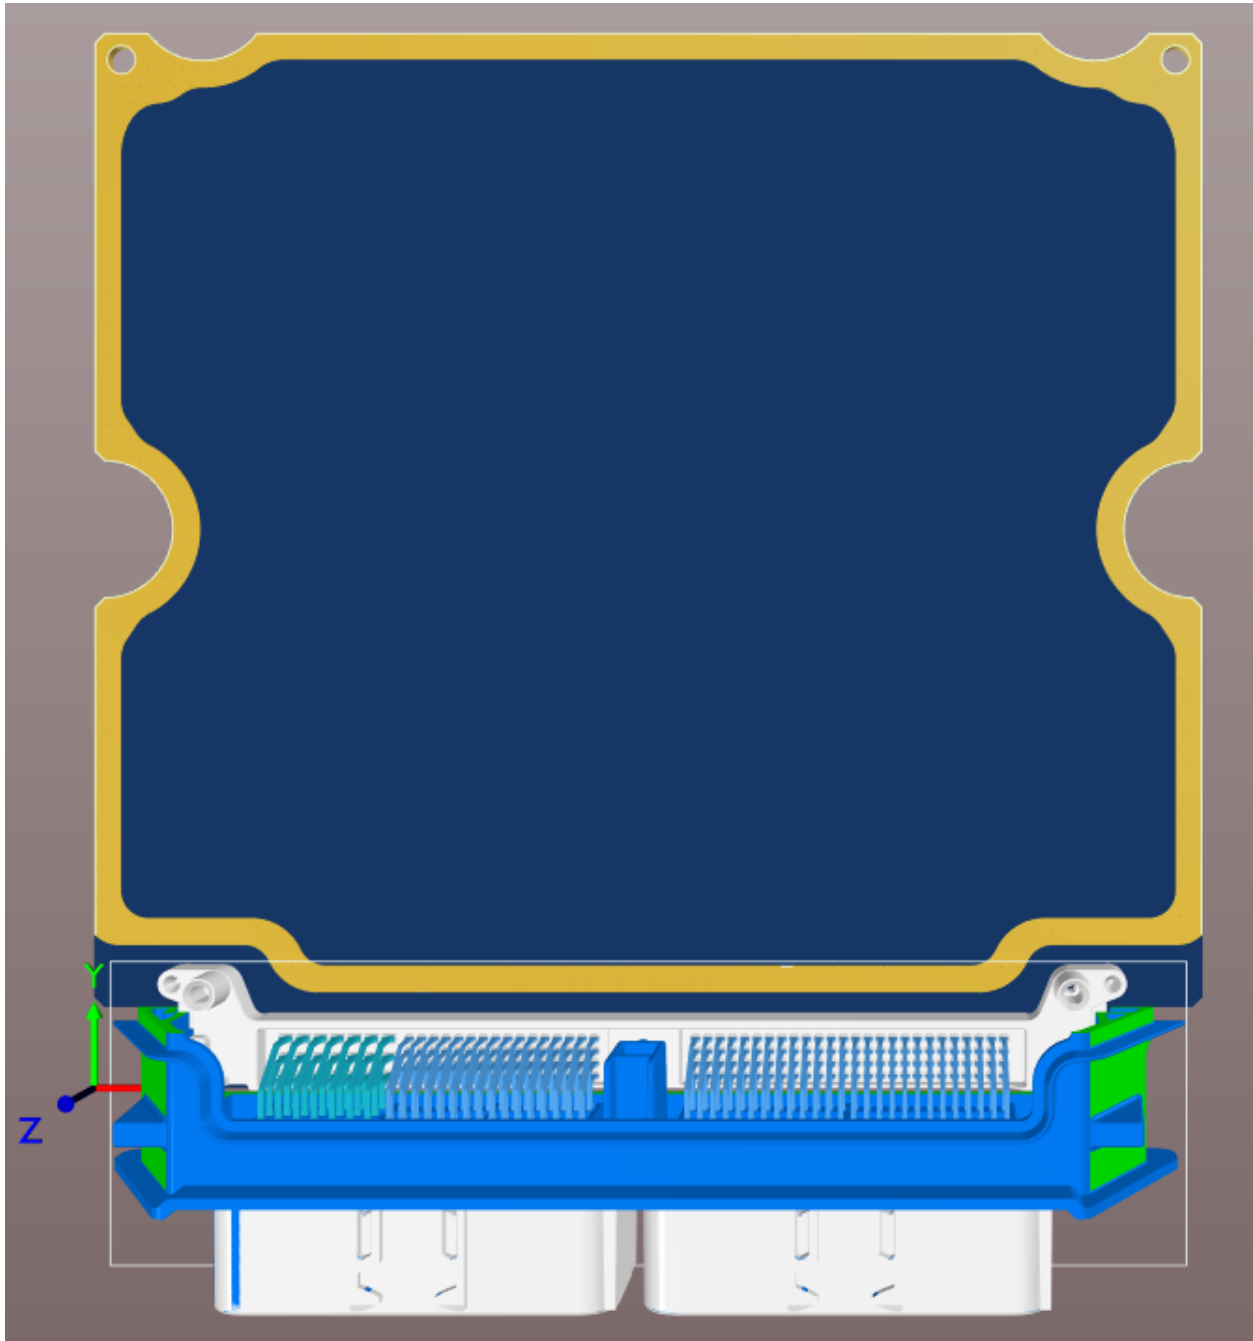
D(C) PCB Kontur mit Kupferfläche, Oberseite
